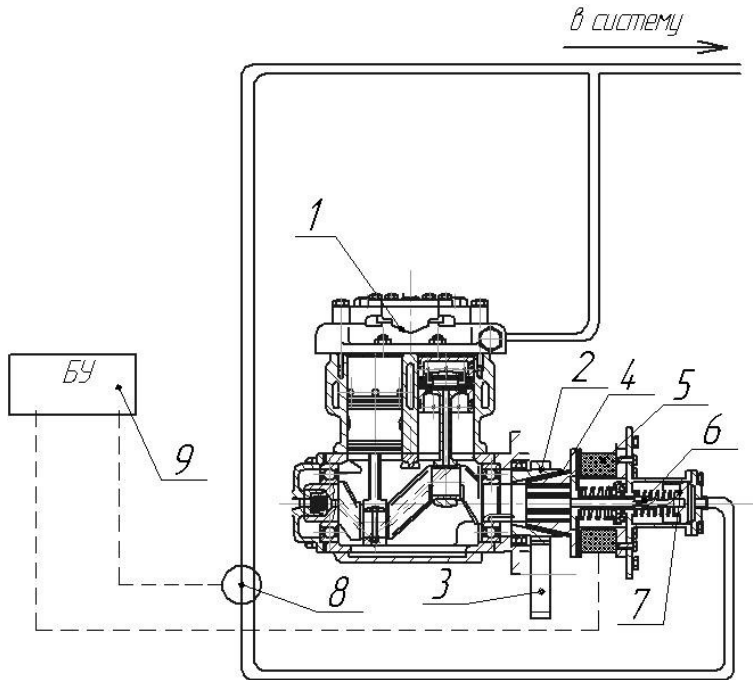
Компрессор с устройством автоматического отключения привода.
